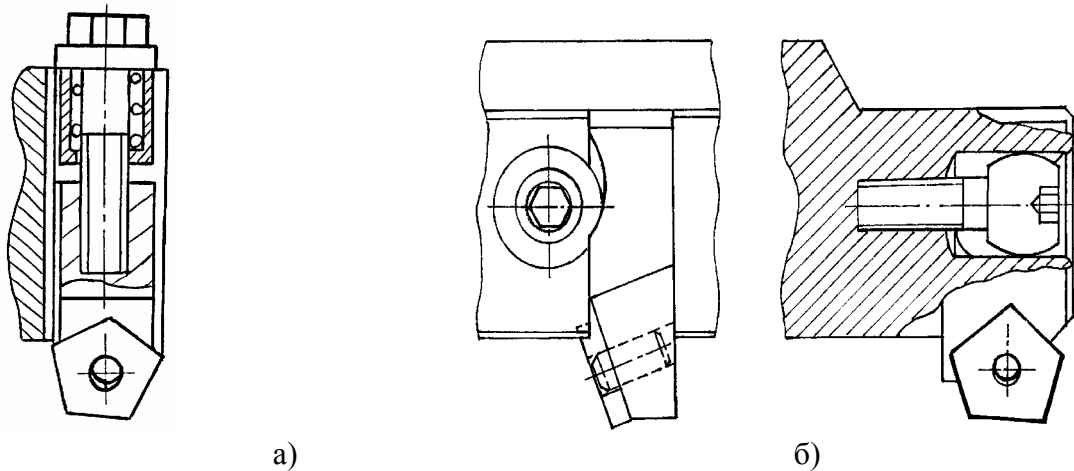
Конструкции торцовых фрез с совместным креплением ножа и пластин
